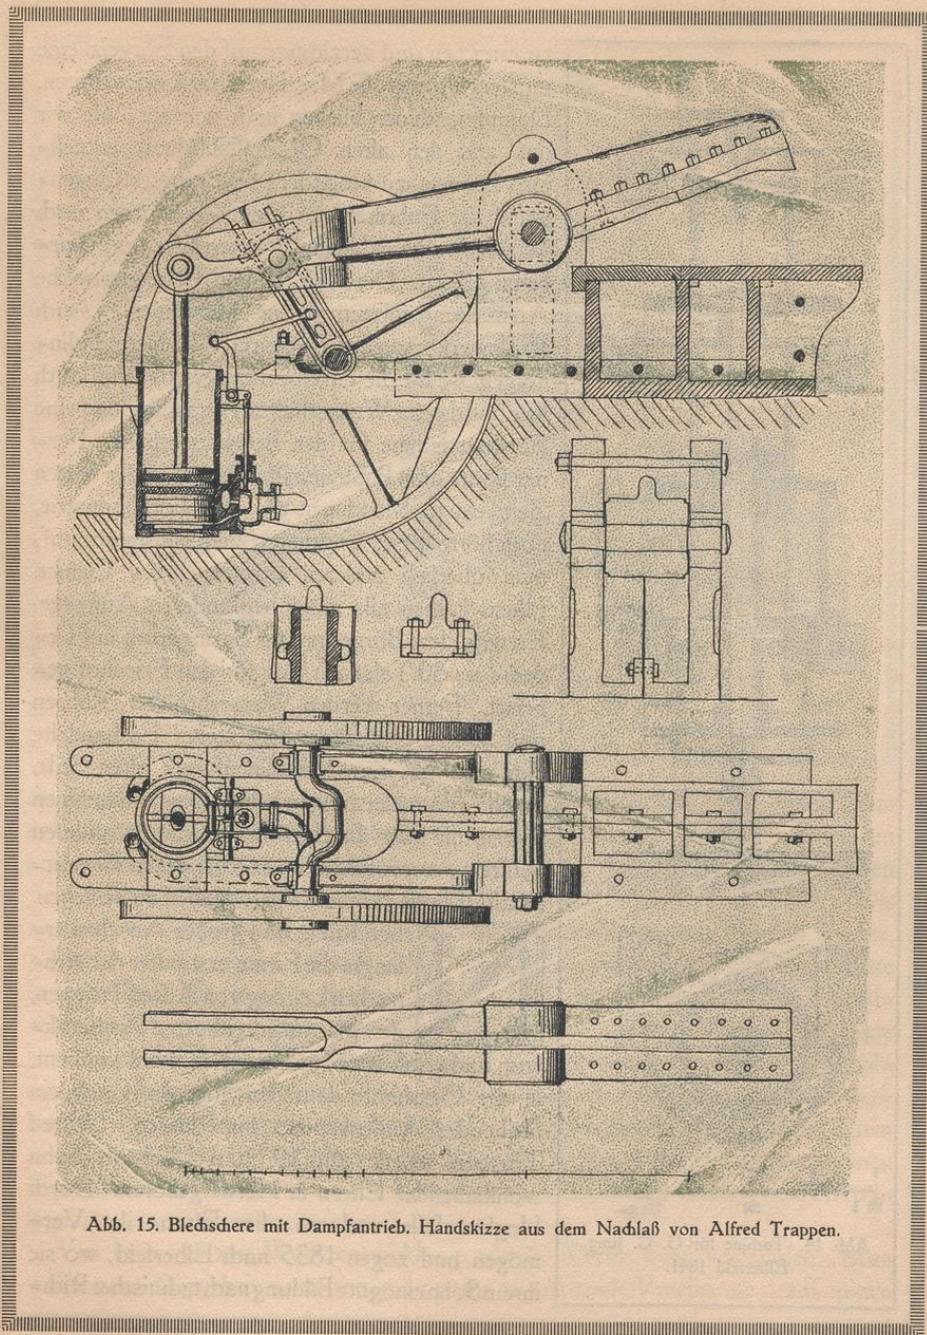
Bleischere mit Dampfantrieb. Handskizze aus dem Nachlaß von Alfred Trappen.
